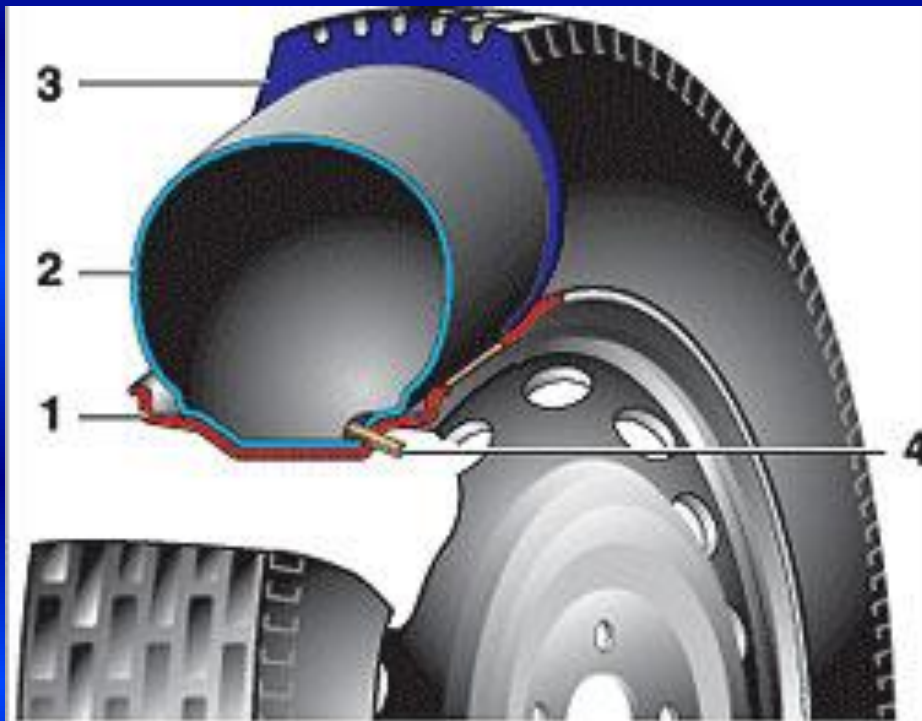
Конструкция колеса с камерной шиной: 1 – обод колеса; 2 – камера; 3 – шина (покрышка); 4 – вентиль.
